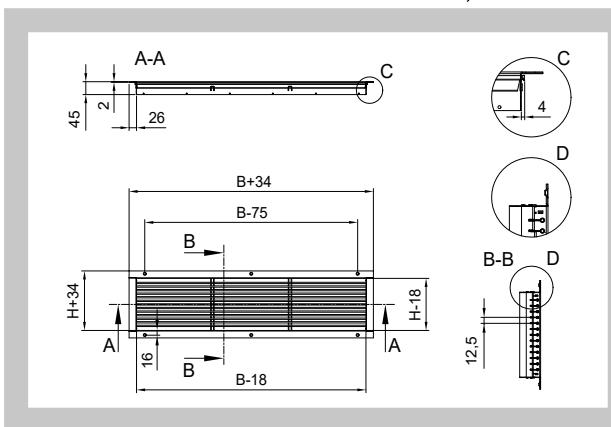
Feste Lamellen - Lamellenabstand 20 mm
